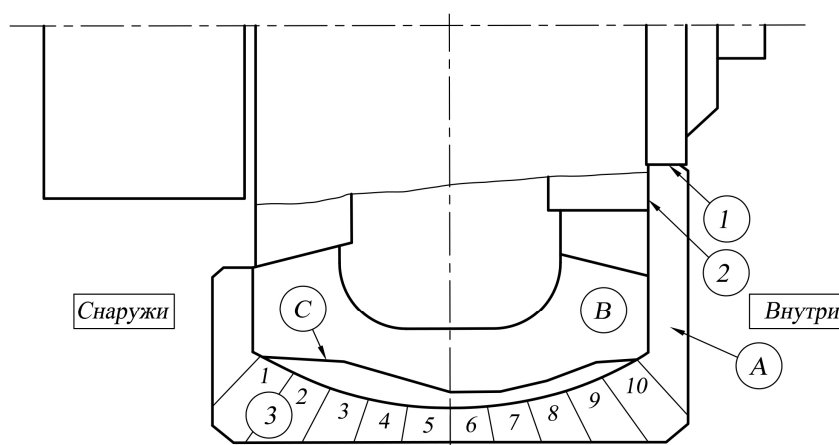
Схема измерения износа рабочей поверхности бандажа валка мельницы: А — шаблон для бандажа; В — бандаж мелющего валка; С — линия фронта износа бандажа; 1, 2 — базовые поверхности; 3 — маркировочные линии, в направлении которых измеряется величина износа; “внутри” — сторона бандажа валка относительно вертикальной оси мельницы
